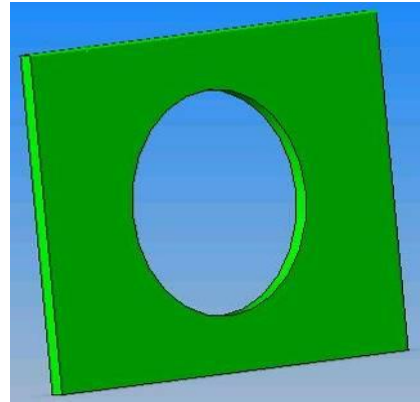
plaques taraudées soudées sur les tubes
